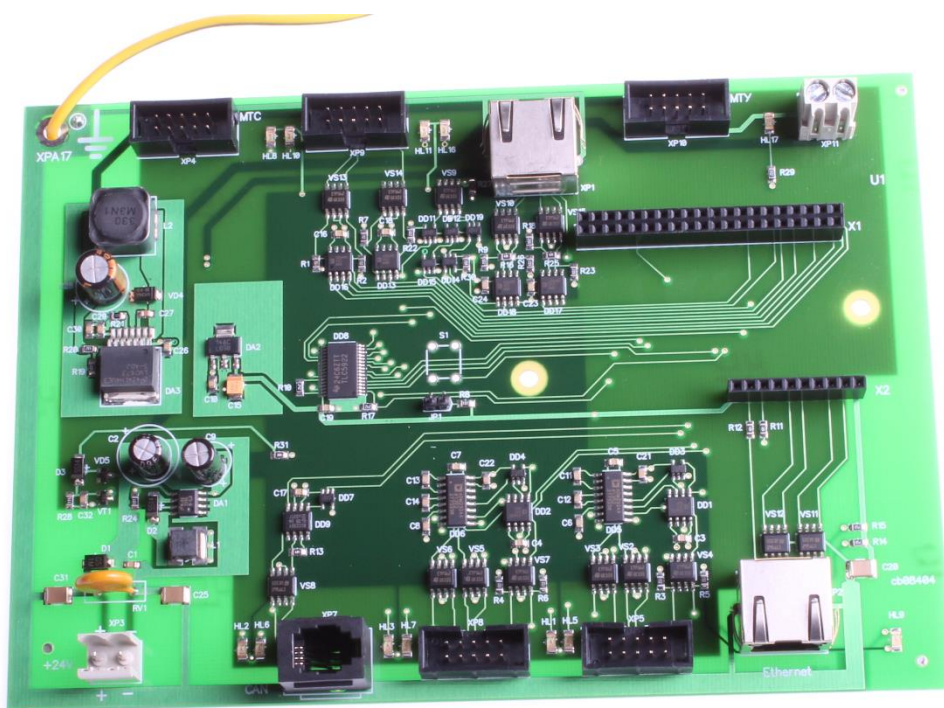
Внешний вид «Синком-ДК» (версия 1, без корпуса, без процессорного модуля)
